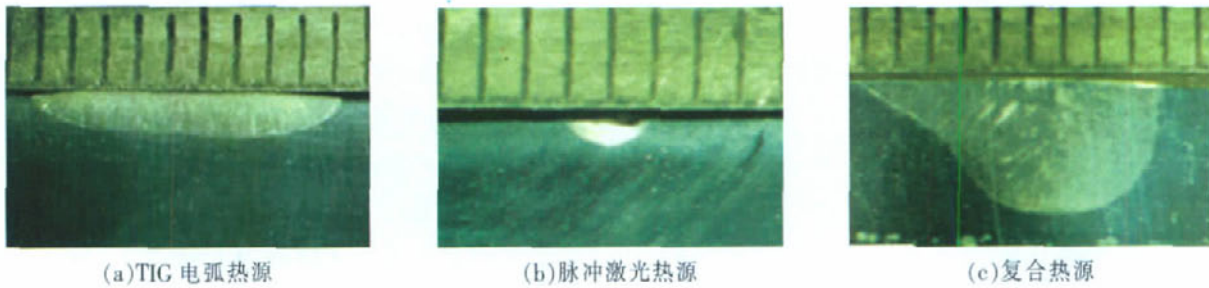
用3种热源得到的焊缝熔池宏观形貌
